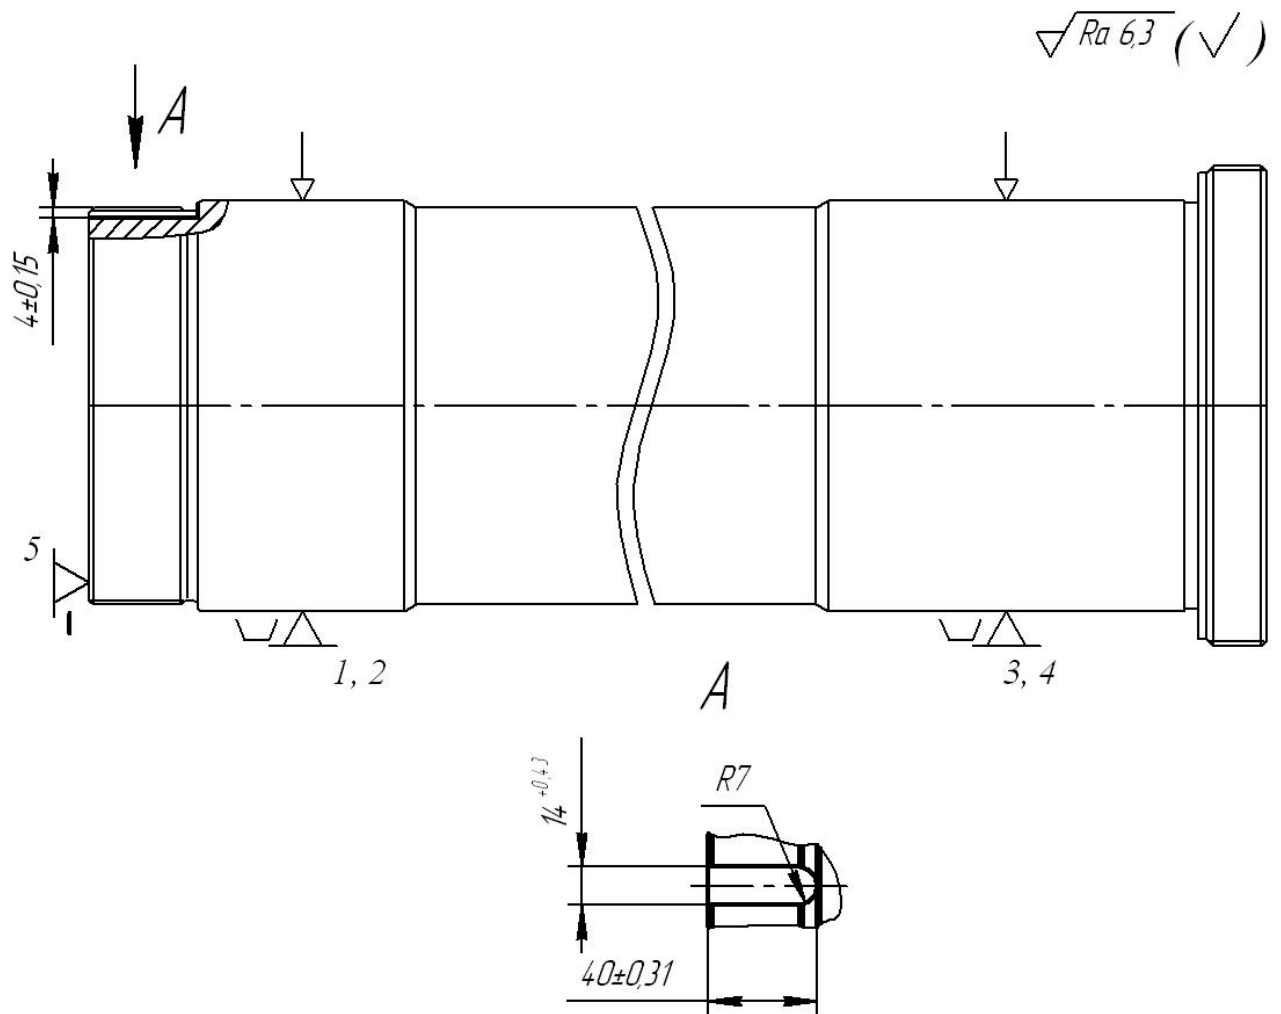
Схема базування заготовки на операції фрезерній з ЧПК 040
